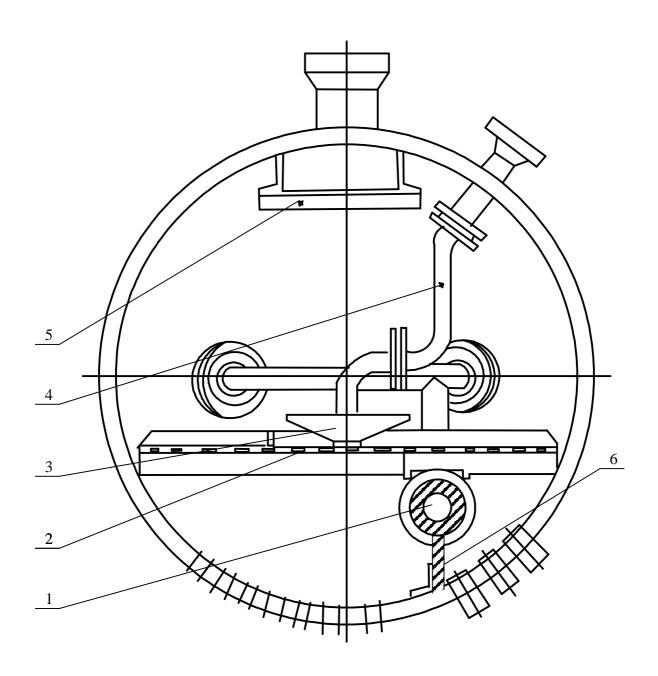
Паровой коллектор котла КВВА-12/28: 1 – питательная труба; 2, 5 – дырчатые щиты; 3 – воронка; 4 – труба верхнего продувания; 6 – разделительный щит
